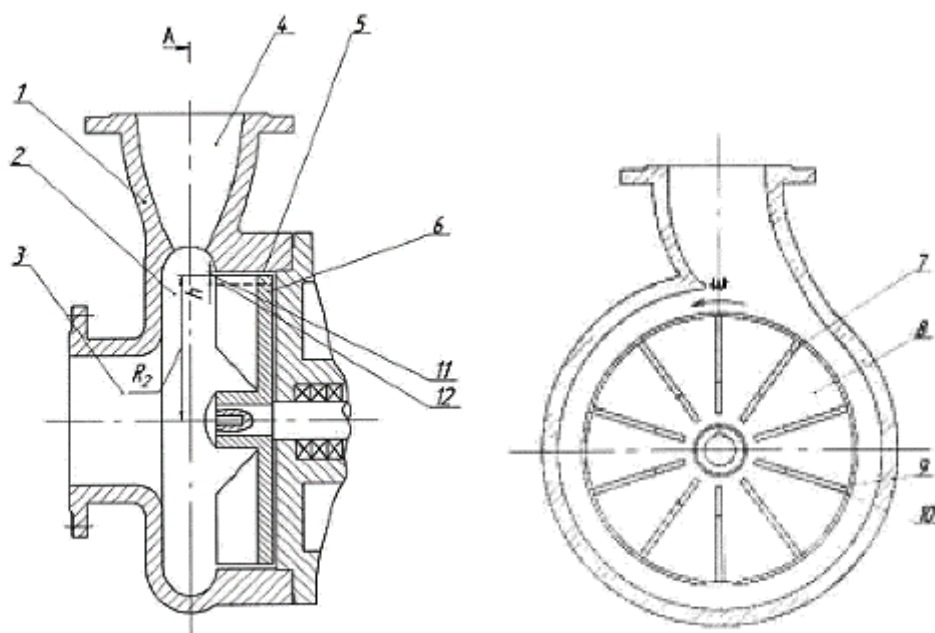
Насос за пат. № UA 73533 U: 1 – корпус; 2 – камера; 3, 4 - всмоктувальний та напірний патрубки; 5 – циліндрична розточка; 6 – робоче колесо; 7 – лопать; 8 - міжлопатеві канали; 9, 10 - робоча і тильна сторона колеса; 11 – щілина; 12 - підрізка по зовнішньому діаметру робочого колеса
